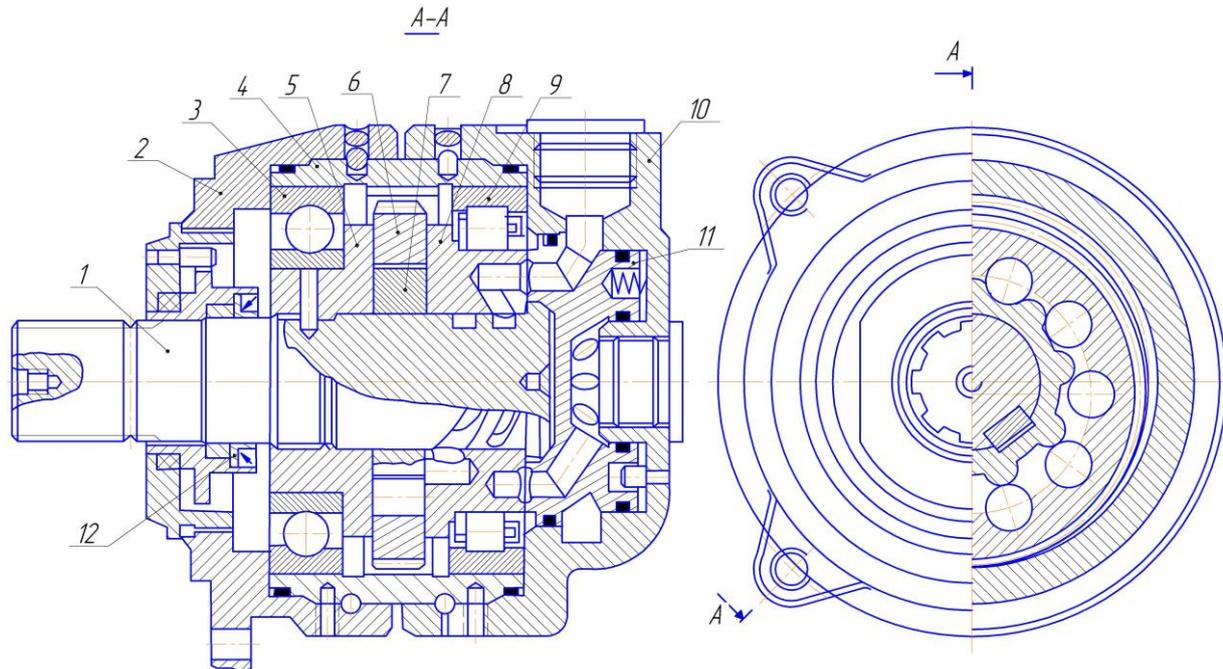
Планетарний гидромотор серії ГПР-Ф: 1 – вал; 2 – передня крышка; 3 – подшипник радіально-упорний; 4 – корпус; 5 – щека; 6 – охоплюючий витеснитель (ротор); 7 – охоплюваний витеснитель (шестерня); 8 – розподільник; 9 – подшипник роликів радіальний; 10 – задня крышка; 11 – золотник; 12 – ущільнювальний вузол.
